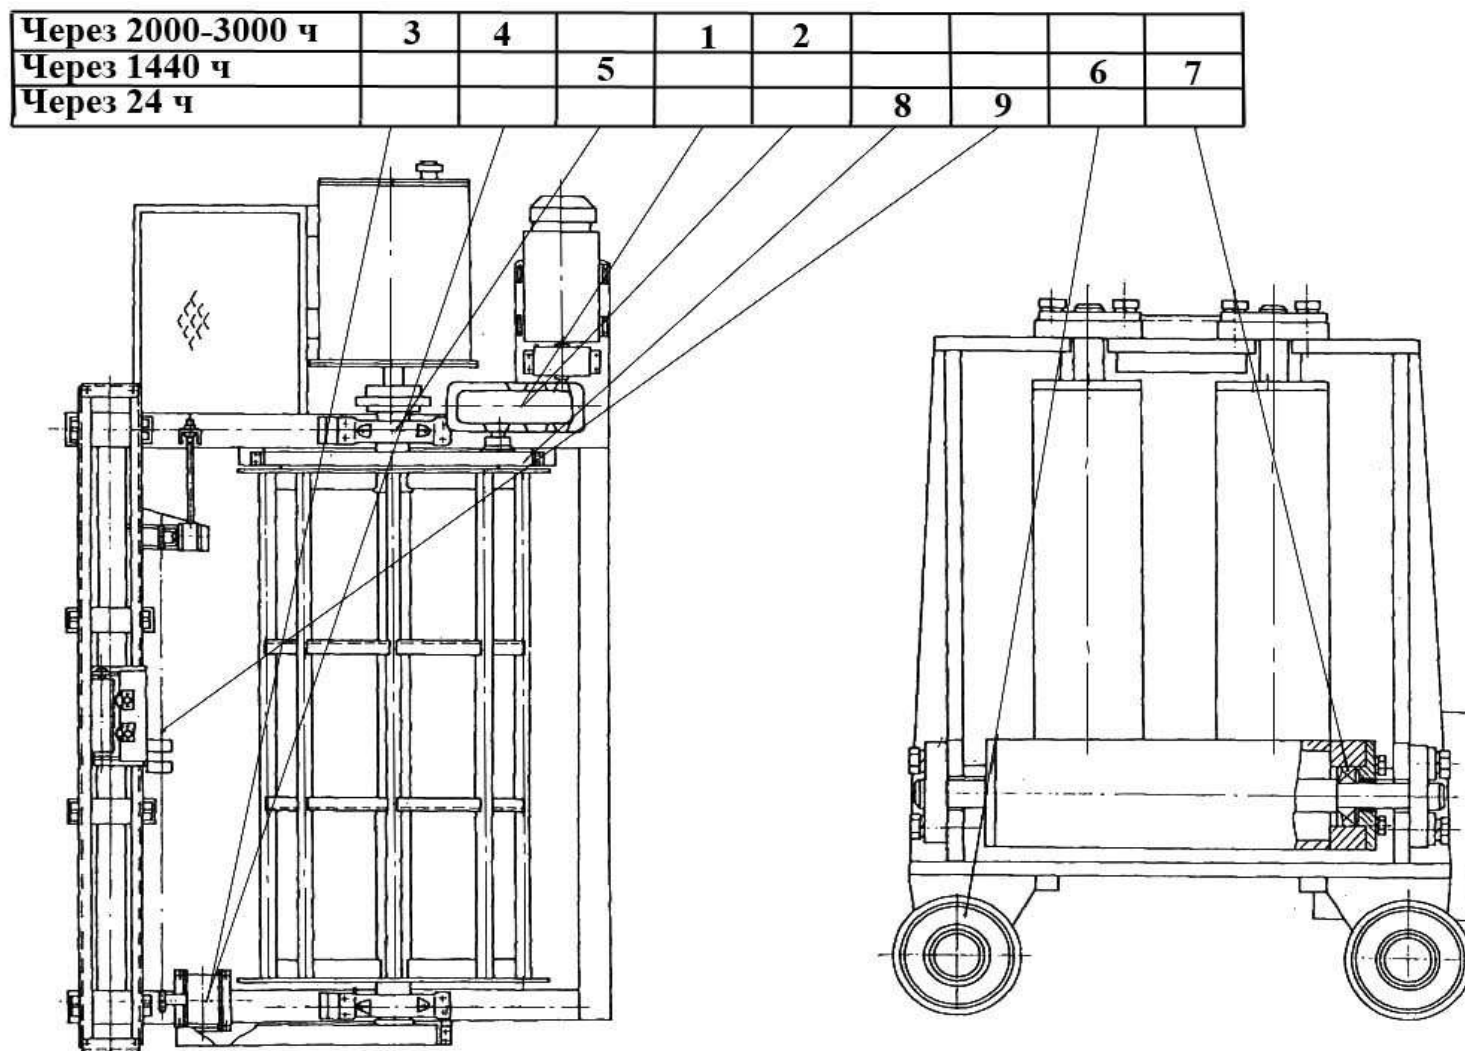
Схема смазки кабельного барабана экскаватора ЭКГ-10
